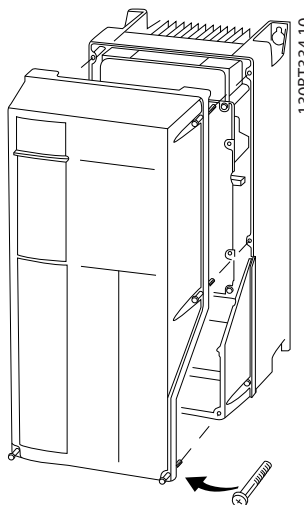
Acceso al cableado de las protecciones IP55 e IP66
